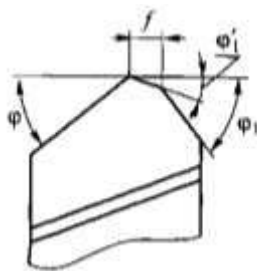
Заточення вершини токарного різця для вібраційного точіння.
